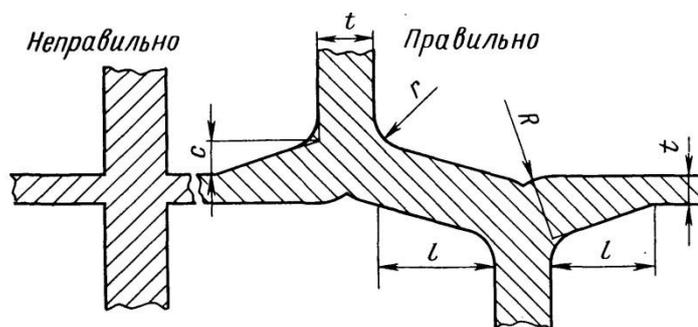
Неправильное и правильное выполнение узла пересечения стенок
